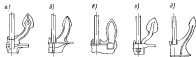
Типы якорей бесштоковых: а — Крюков; б — Юнкер; в — Байер-Виндмилл; г — Тейлор; д — Спок
